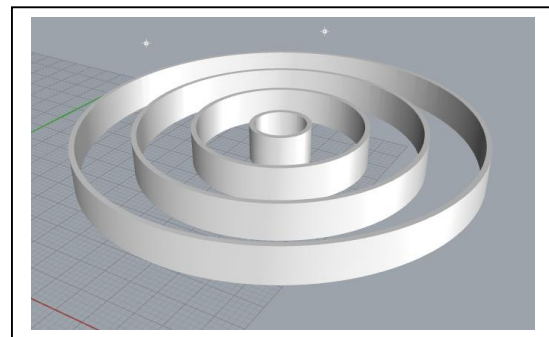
Molde diseñado en Rhino para imprimir en 3D
